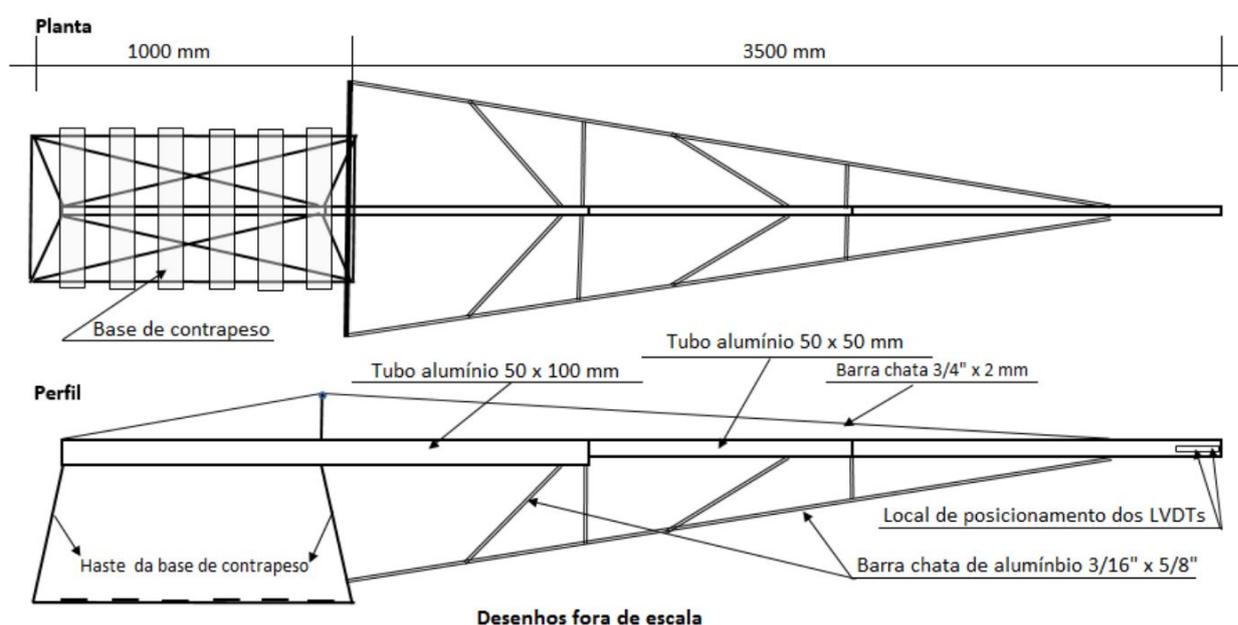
Desenho da Treliça de Suporte (em planta e em perfil)
